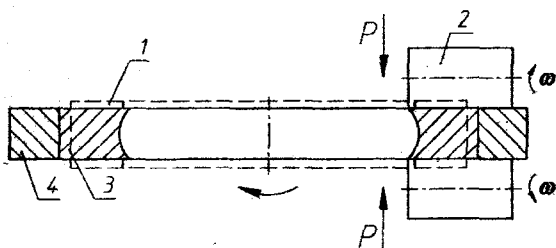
Раскатка колец при воздействии валков на торцы заготовки
